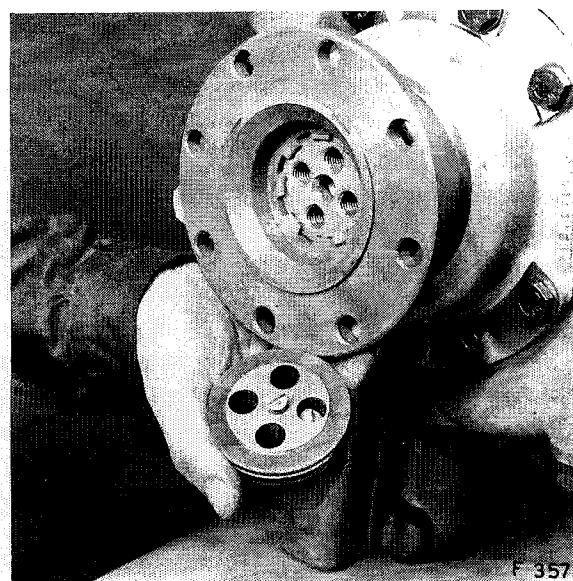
Druckscheibe mit O-Ring und aufgeschraubten Folien
